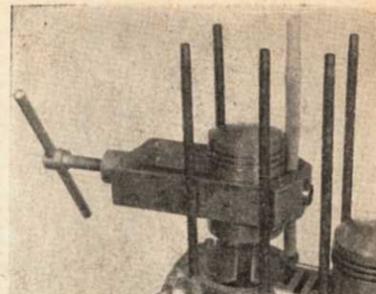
Démontage de l'axe de piston avec extracteur n° 1.115. — Repérer positions de l'axe et du piston
